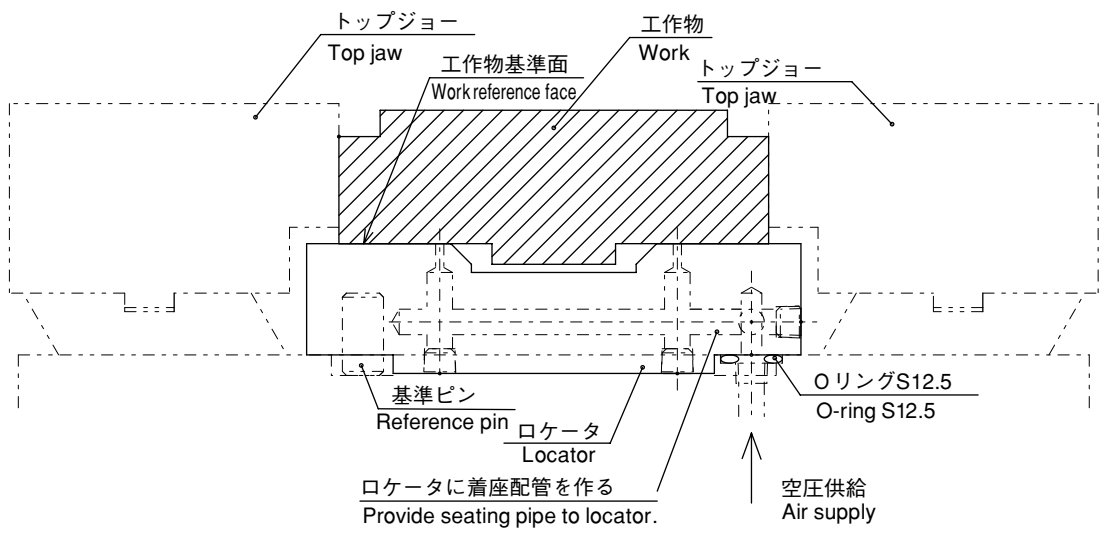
着座検知とロケータ取付け Seating detection and locator mounting
